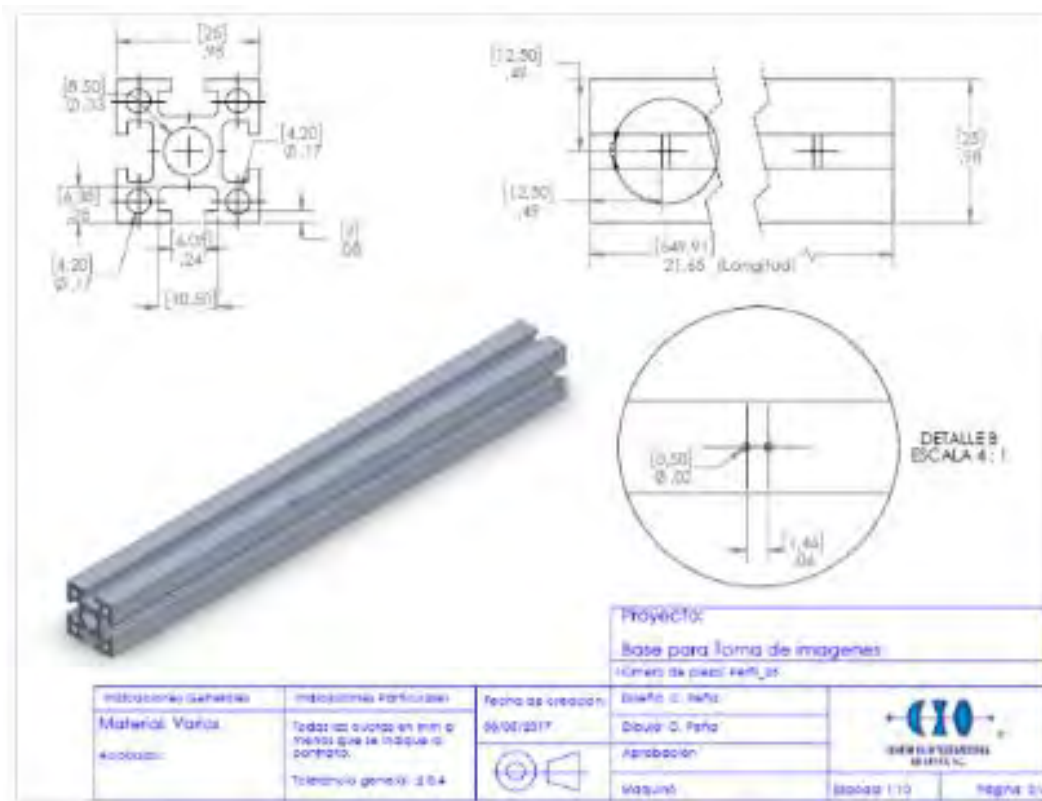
Perfil de aluminio 25 mm para estructuras modulares.
